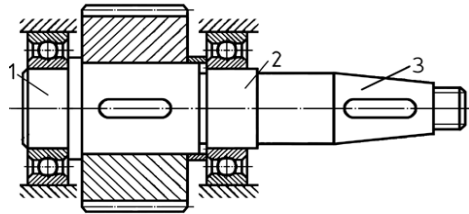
Кінцеві цапфи: 1 – шип; 2 – шийка; 3 – конічний кінець вала
